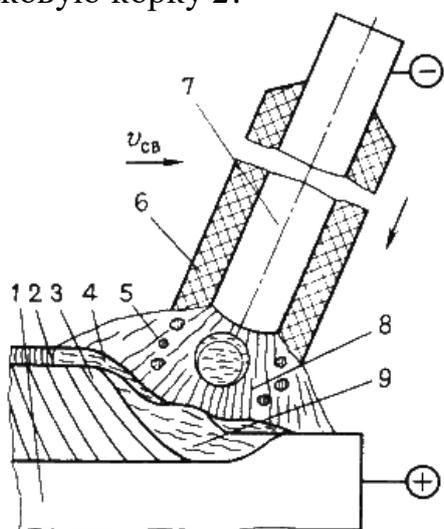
Схема процесса сварки металлическим покрытым электродом
